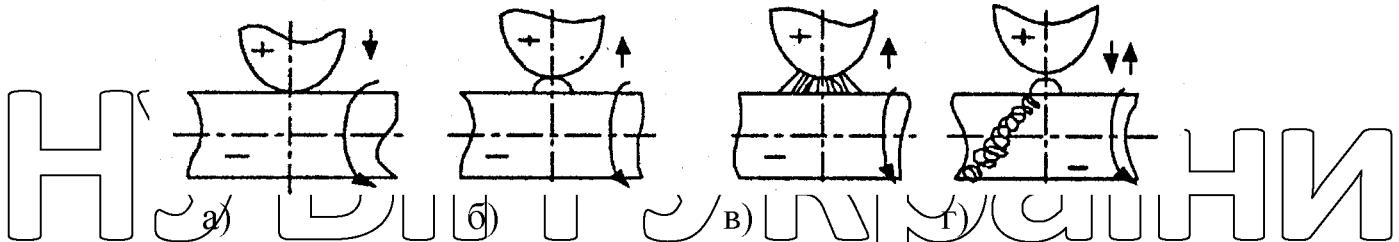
Схеми для формування валика за вібродугового наплавлення.
